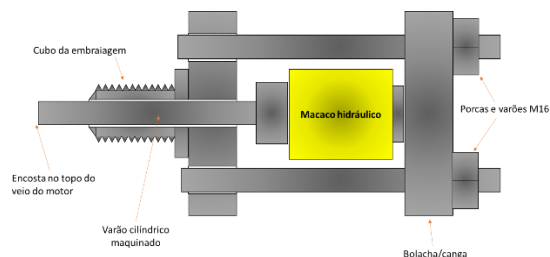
Ferramenta idealizada para desmontagem de acoplamento hidráulico
